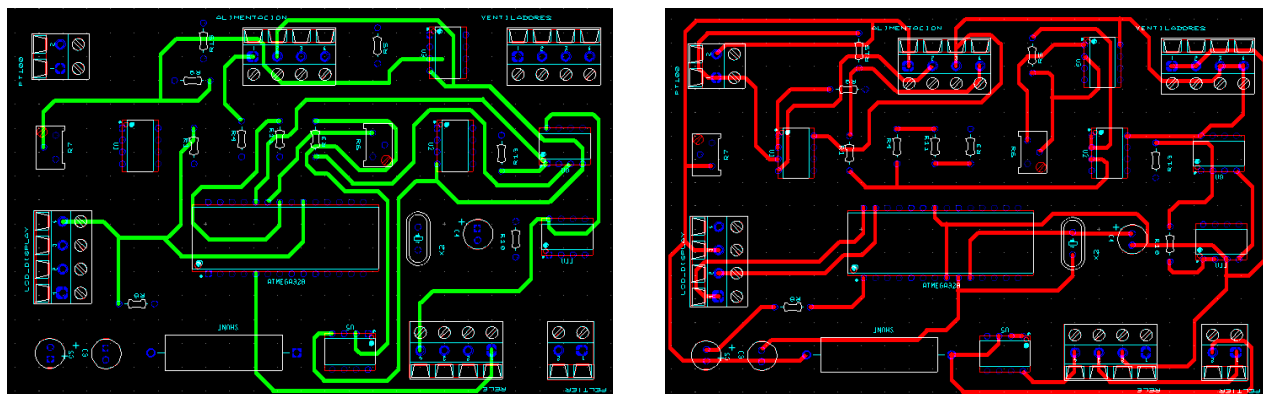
Layout caras TOP y BOTTOM con pistas de cobre en ambas caras.
